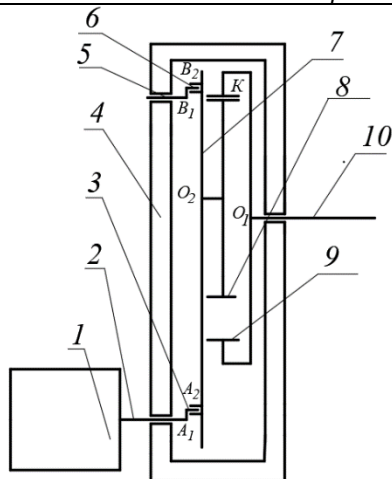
Кинематическая схема эксцентриковой передачи с параллельным расположением входного и выходного валов
